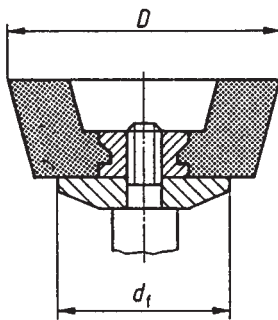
Aufspannen von kegelligen Schleiftöpfen mit Gewindeinsatz
